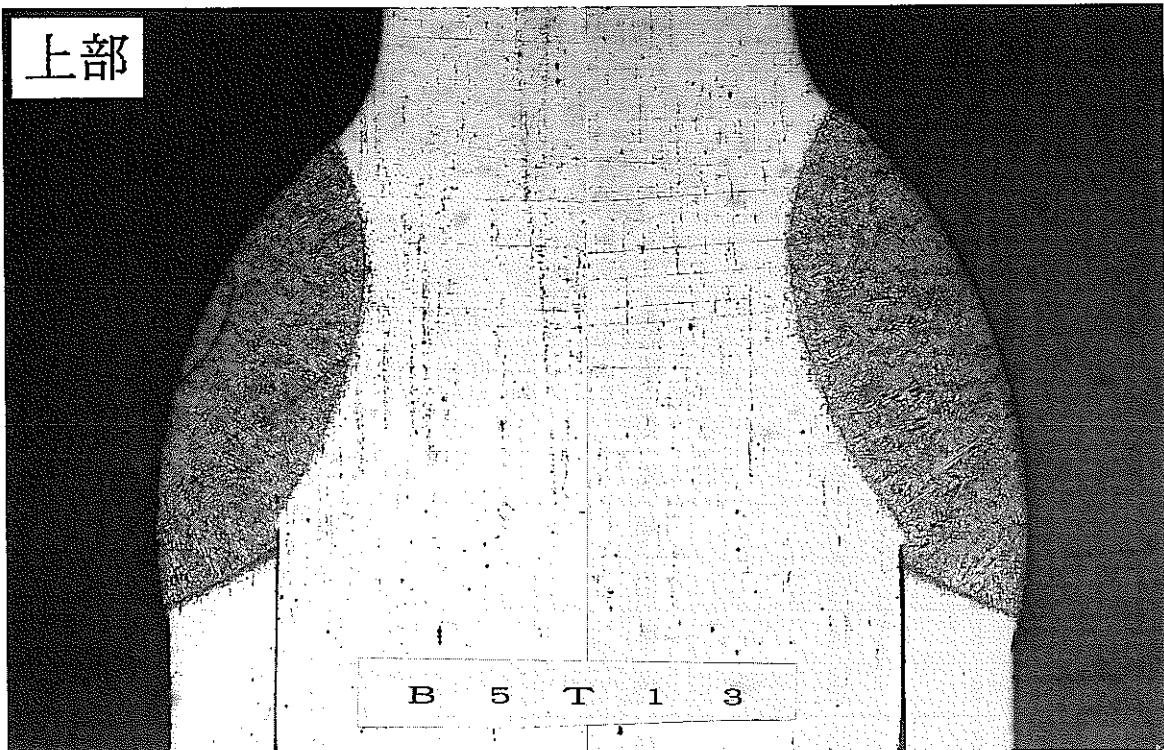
上・下部端栓溶接施行断面金相写真
